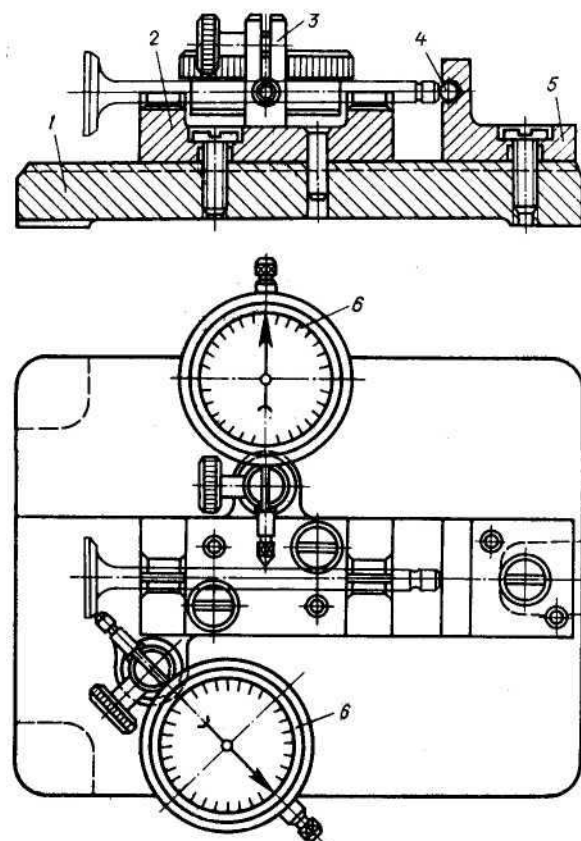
Проверка клапана на concentричность рабочей фаски головки и стержня:
